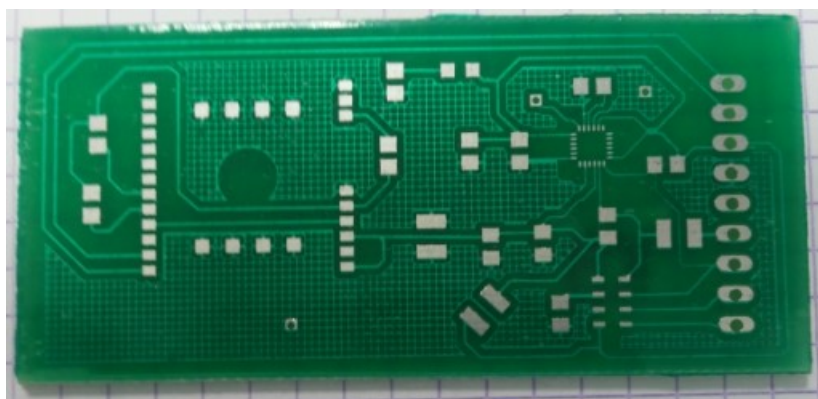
PCB tras aplicar máscara de soldadura.
